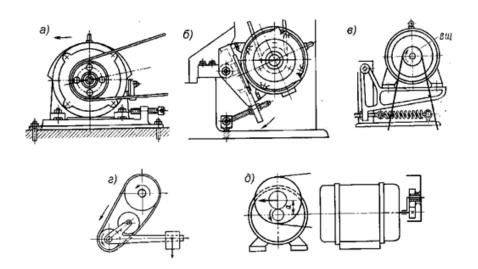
Способы предварительного натяжения приводных ремней
